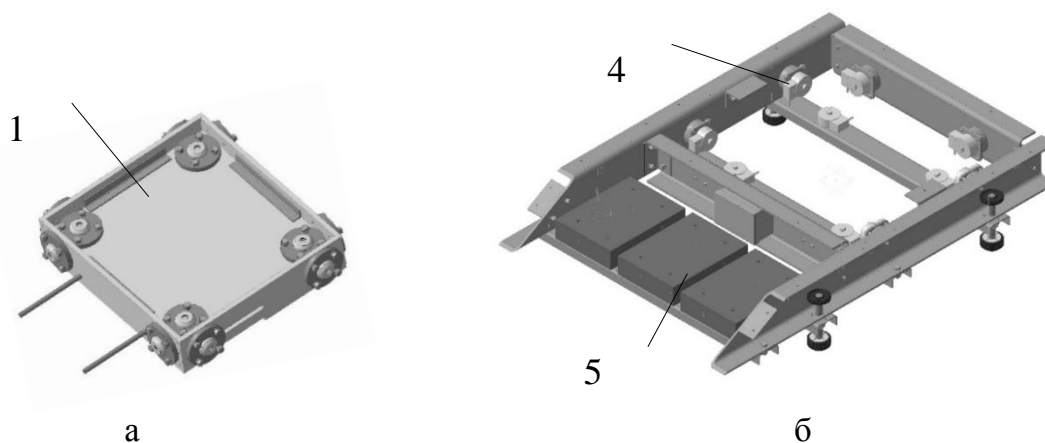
Стенд в сборе с датчиками: а – измерительная платформа с опорными узлами для датчиков (вид снизу); б – основание станда
